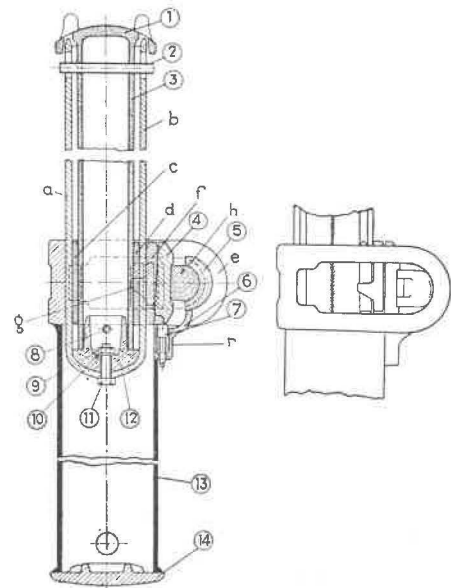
L'étauçon à lamelles Eisenwerk Wanheim.
